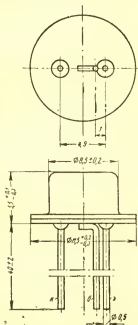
Габаритный чертеж транзисторов П25—П26Б.
